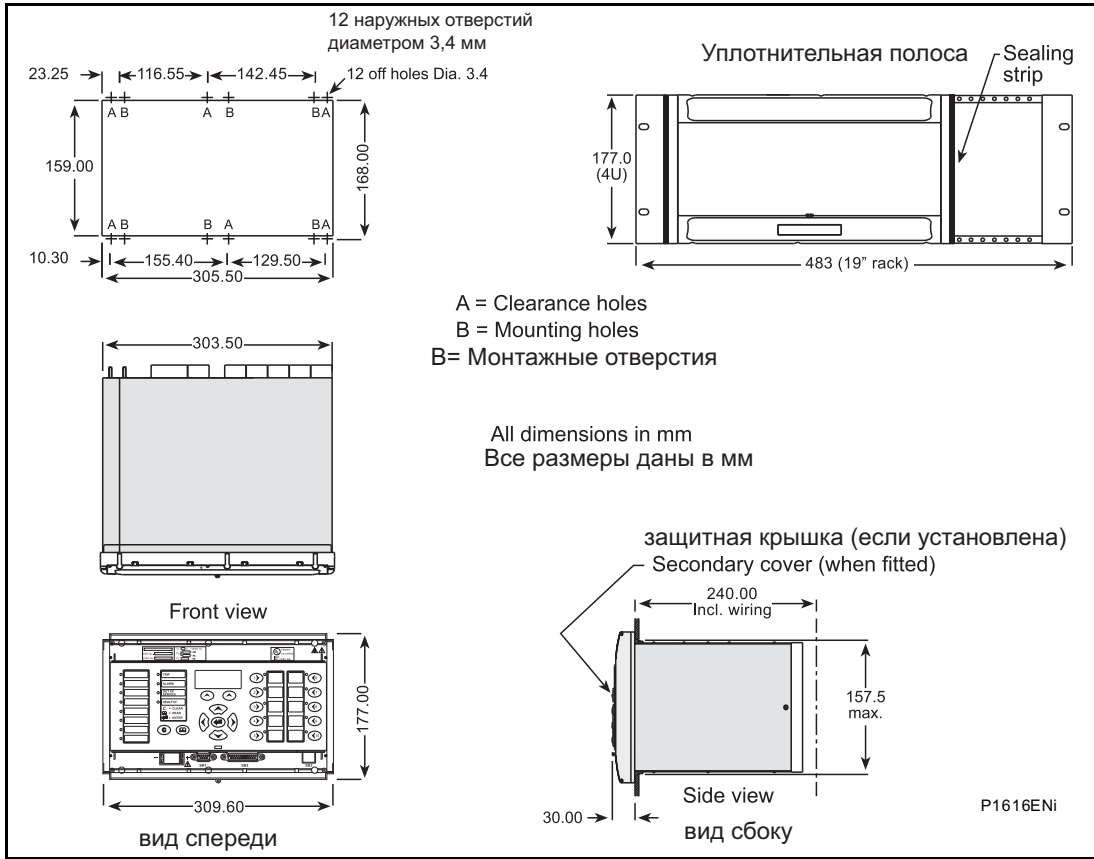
Размеры корпуса P242 (корпус 60TE)
